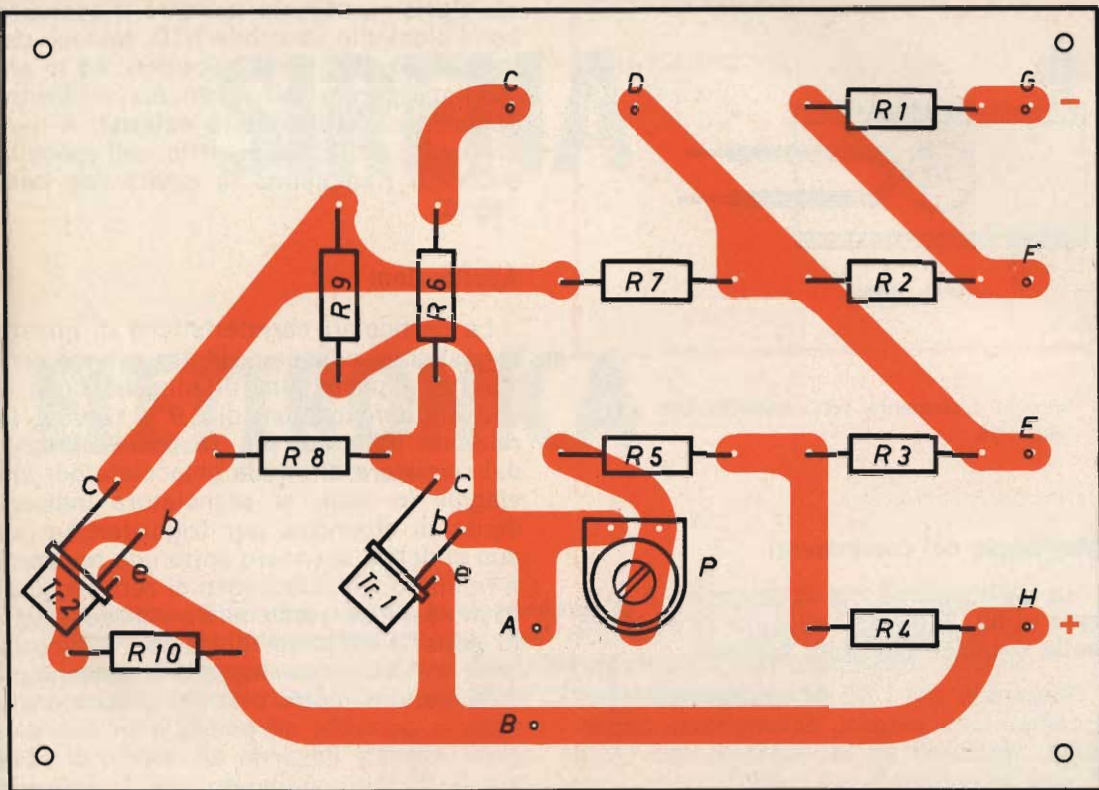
Montaggio dei componenti sul circuito stampato.
